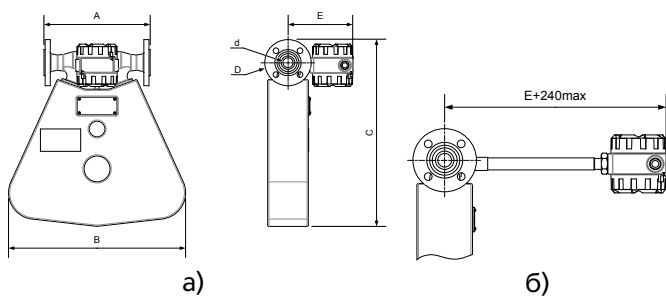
Габариты и присоединительные размеры датчиков Ду25...80:
